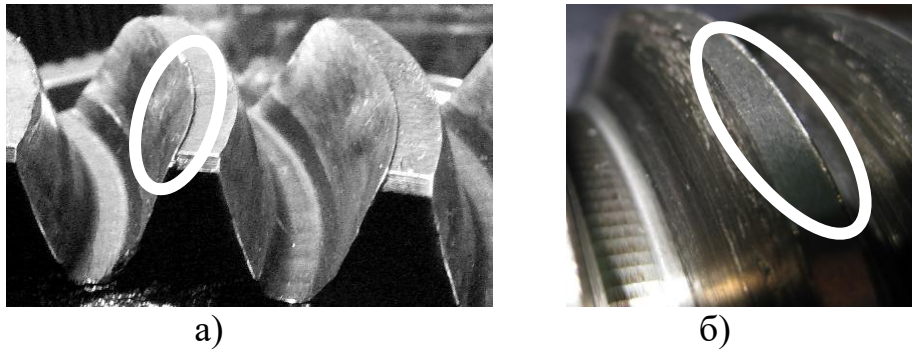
Смятие на вершинах зубьев колеса а) и витков червяка б)
